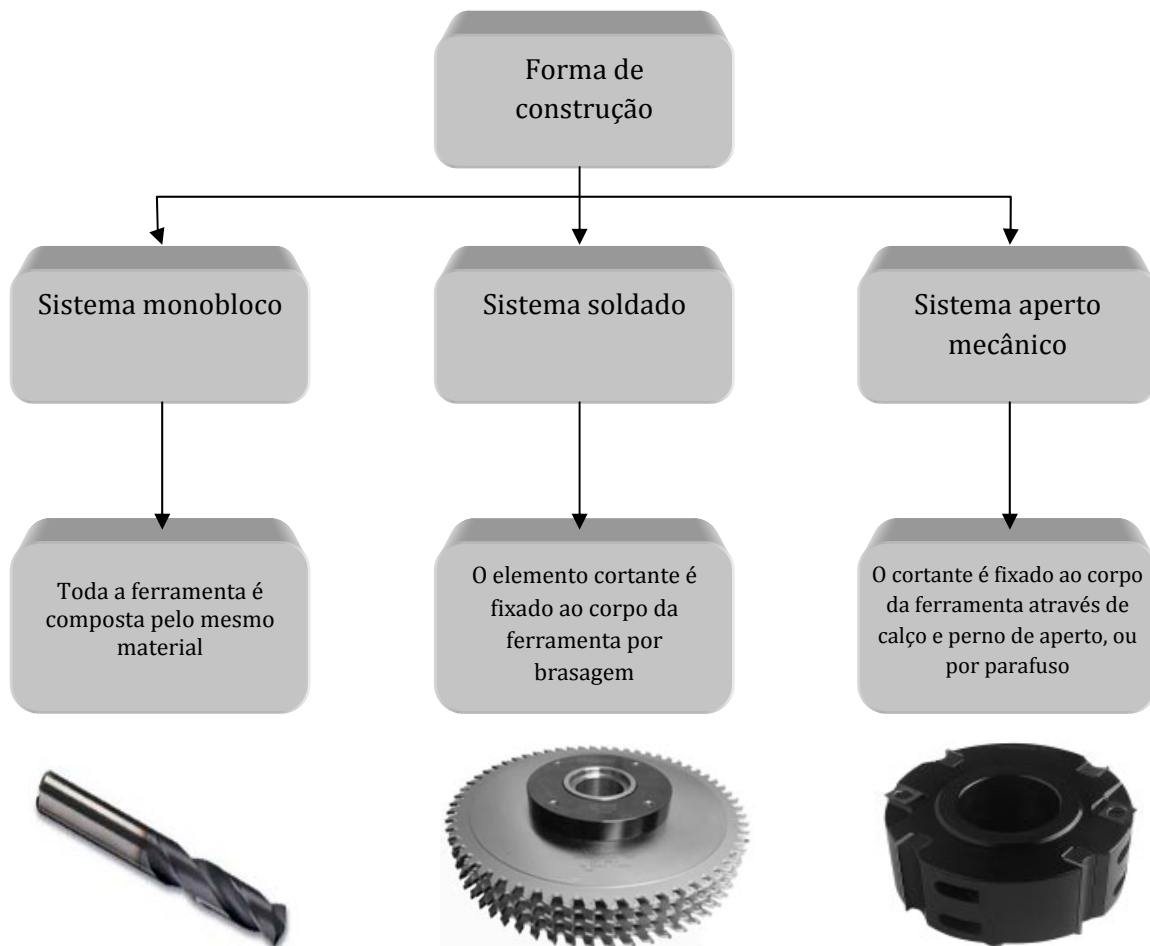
Tipos de construção de ferramentas de corte<sup>[1]</sup>.
